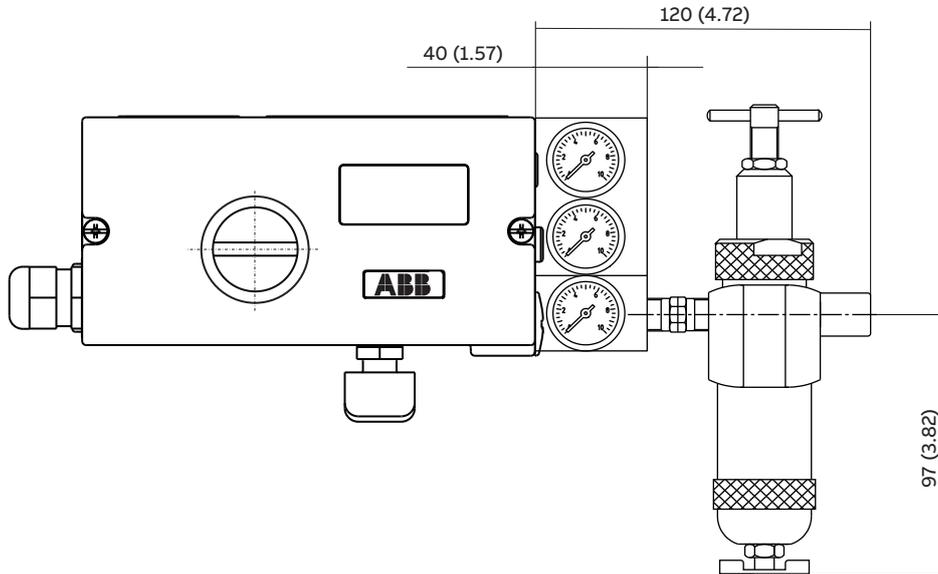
Régulateur de position TZIDC-110 avec bloc manométrique installé et régulateur de filtre
